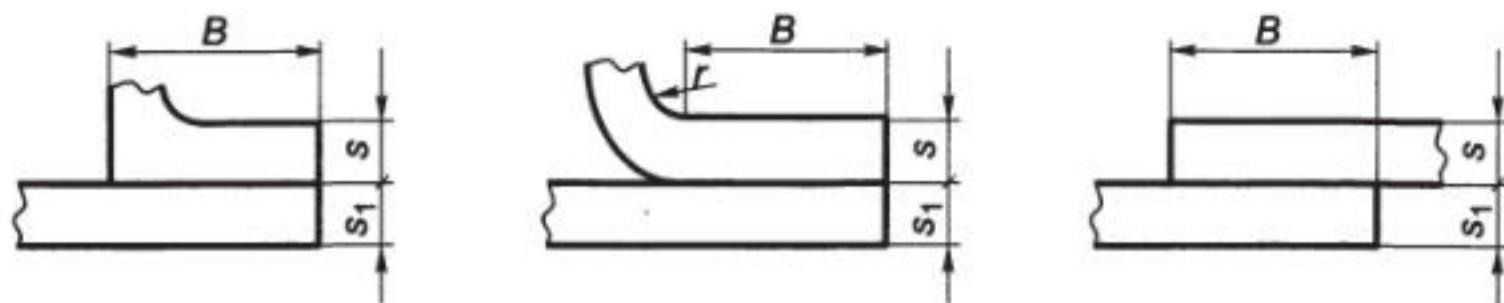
Виды нахлестки деталей для контактной точечной, рельефной и шовной сварки
